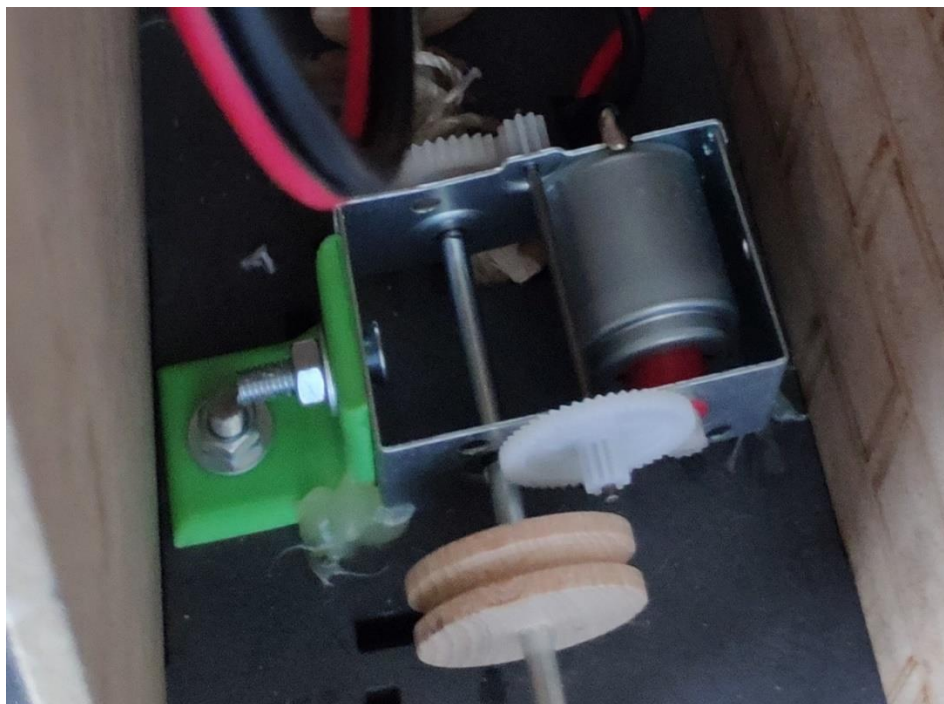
Motor con su anclaje (pieza verde)
